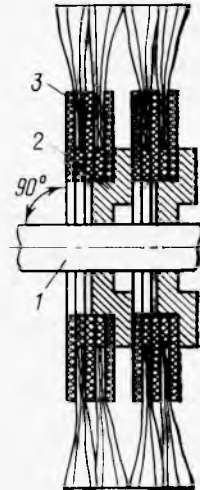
Схема расположения кругов конструкции Костромского ЗДС на валу станка ПИБ:
